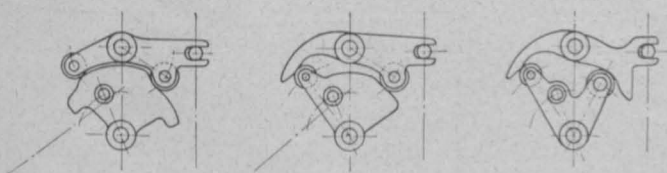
Patente der Prager Maschinenbau-A.-G.
